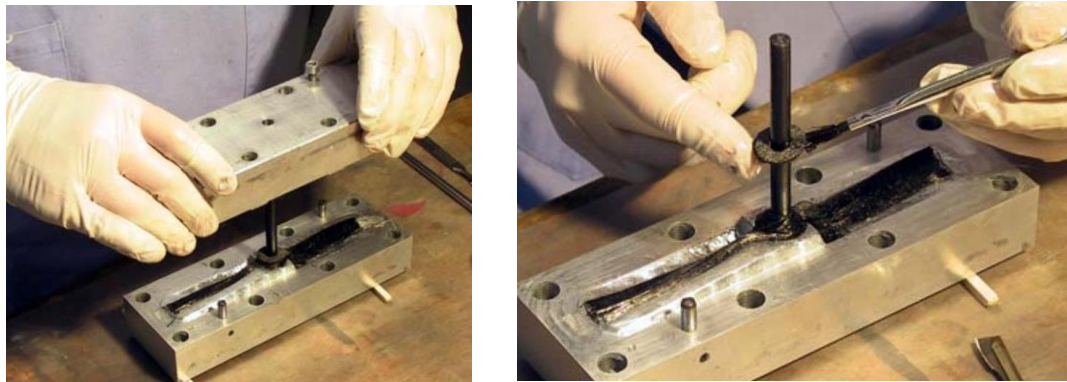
Формування гвинтів у суцільнометалевій прес-формі
